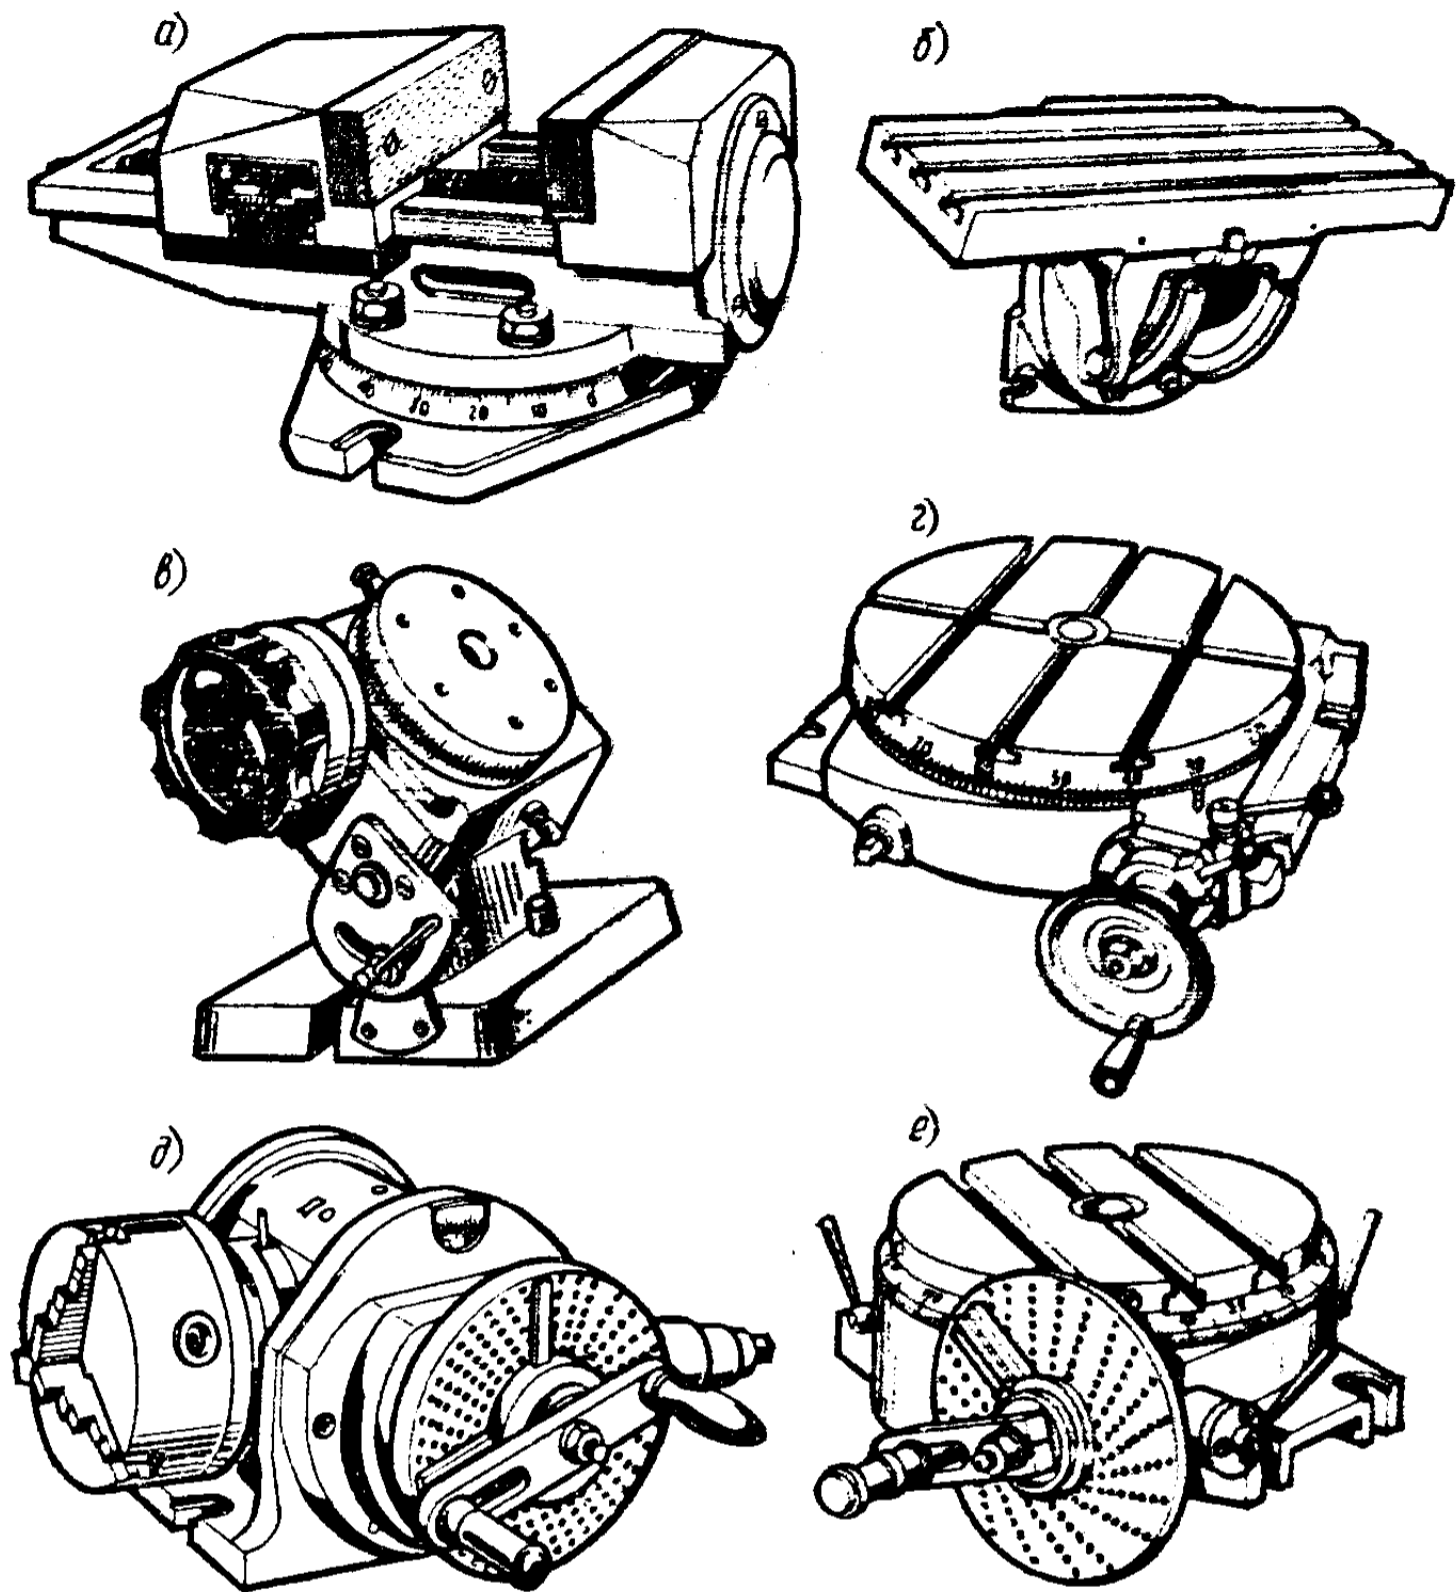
Универсальные приспособления, применяющиеся для обработки заготовок на фрезерных станках:
